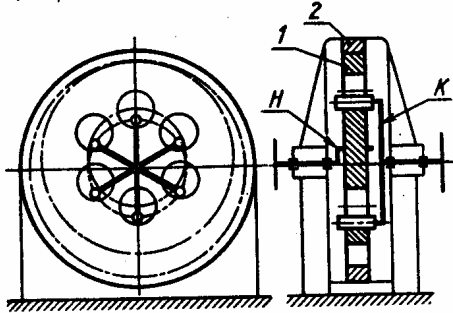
(а). Кинематическая схема планетарного одноступенчатого редуктора с ведущим водилом: валы расположены параллельно установочной плоскости корпуса.
